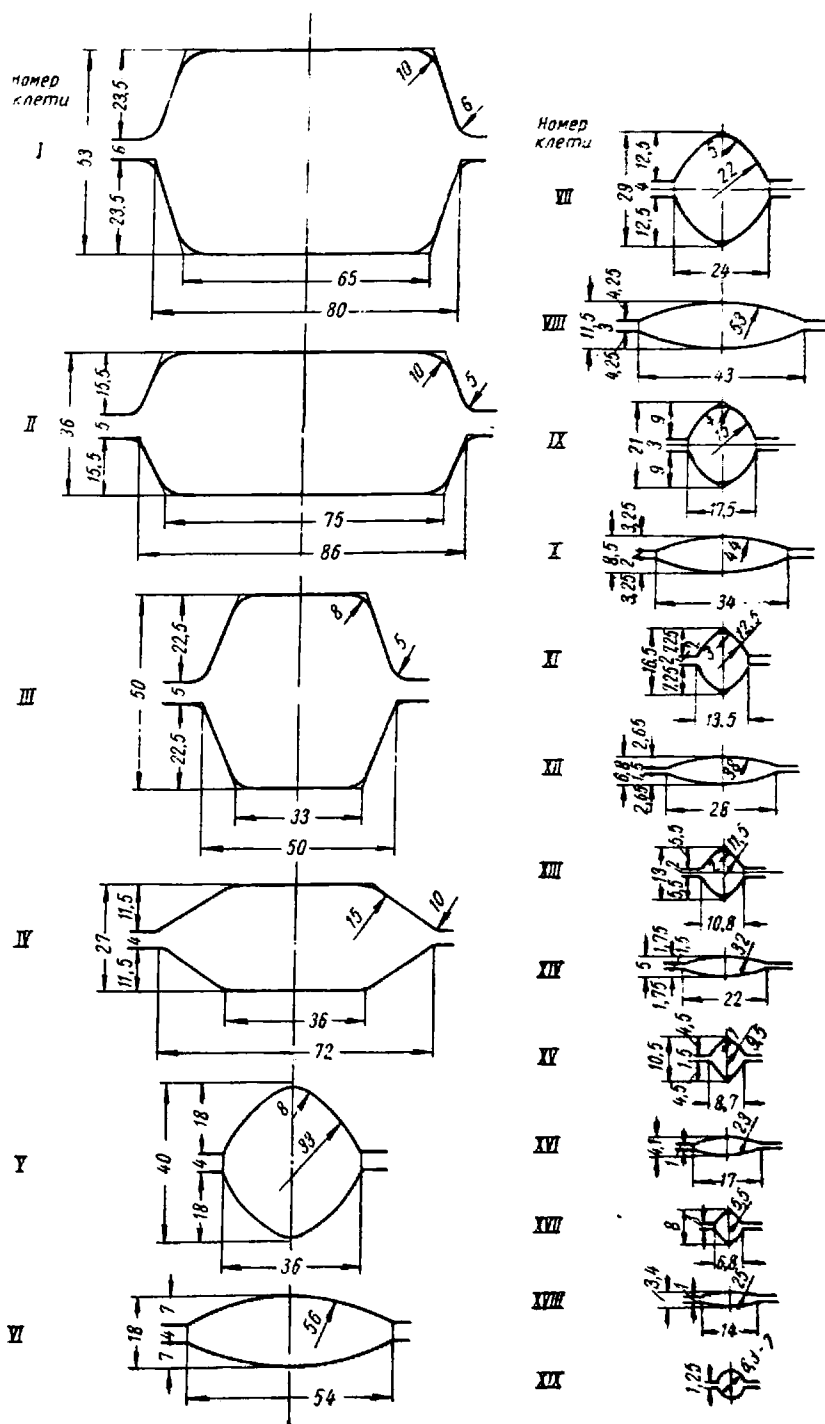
Калибровка валков для прокатки проволоки на непрерывных станах
